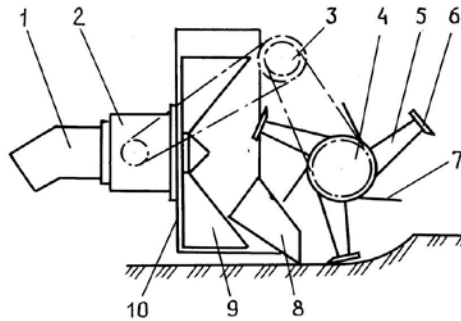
Фрезерно-роторный рабочий орган с цилиндрической фрезой, имеющей горизонтальную ось вращения, перпендикулярную оси канала: 1 – гидромотор; 2 – редуктор; 3 – цепная передача; 4 – фреза; 5 – стойки; 6 – ножи; 7 – лопасти; 8 – направляющее устройство; 9 – лопастный метатель; 10 – окно
